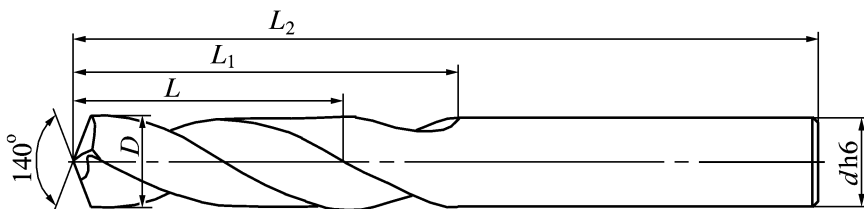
Цельные твердосплавные сверла "SOLIDDRILL"
